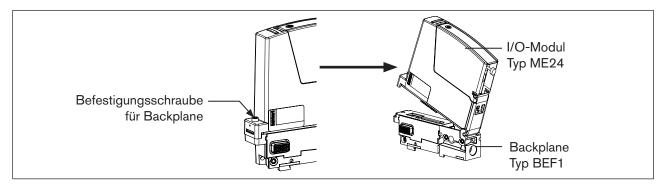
Gerätetausch, I/O-Modul Typ ME24
